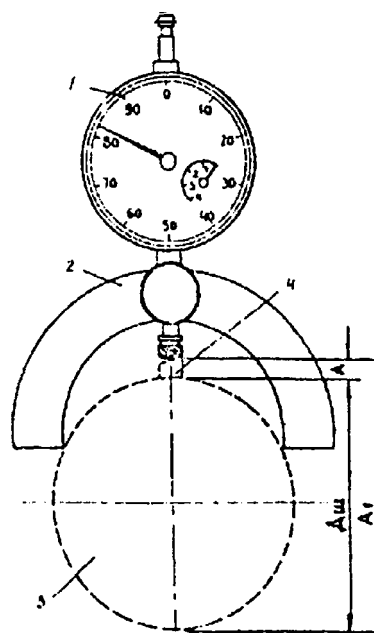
Схема установки резца на размер с помощью индикаторного приспособления:
